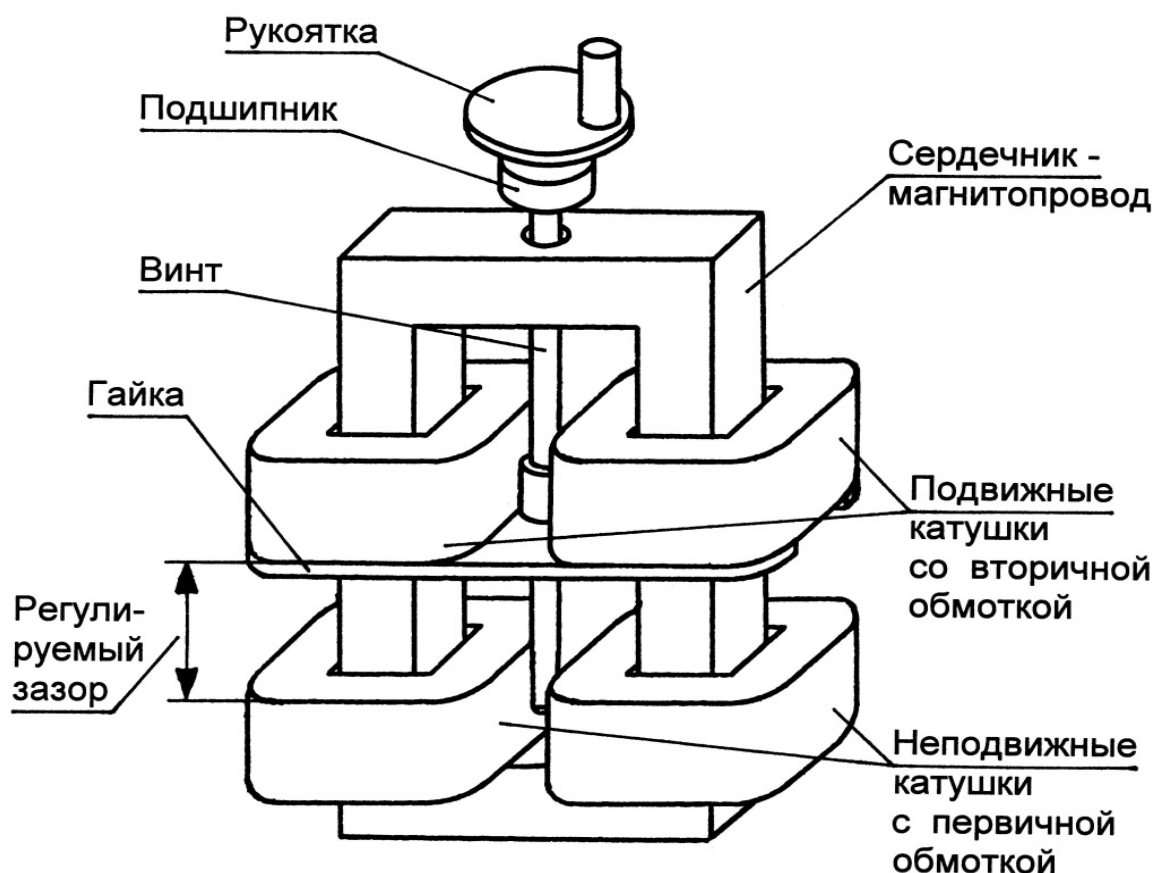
Конструктивная схема сварочного трансформатора с подвижными катушками вторичной обмотки
